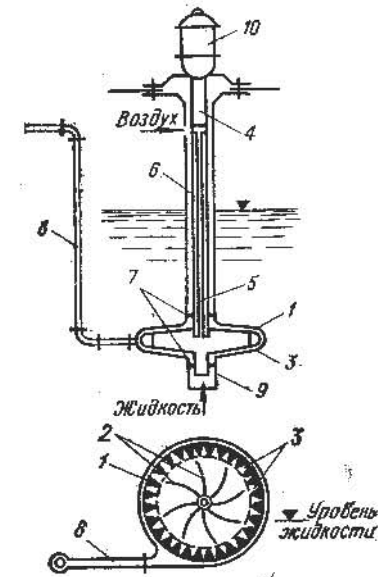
Схема насоса-аэратора: 1 — корпус; 2 — рабочее колесо (крыльчатка); 3 — кольцо с коническими насадками; 4 — вал аэратора; 5 — полость; 6 — кожух вала; 7 — сальники; 8 — напорная линия; 9 — входной патрубок; 10 — привод (двигатель).
